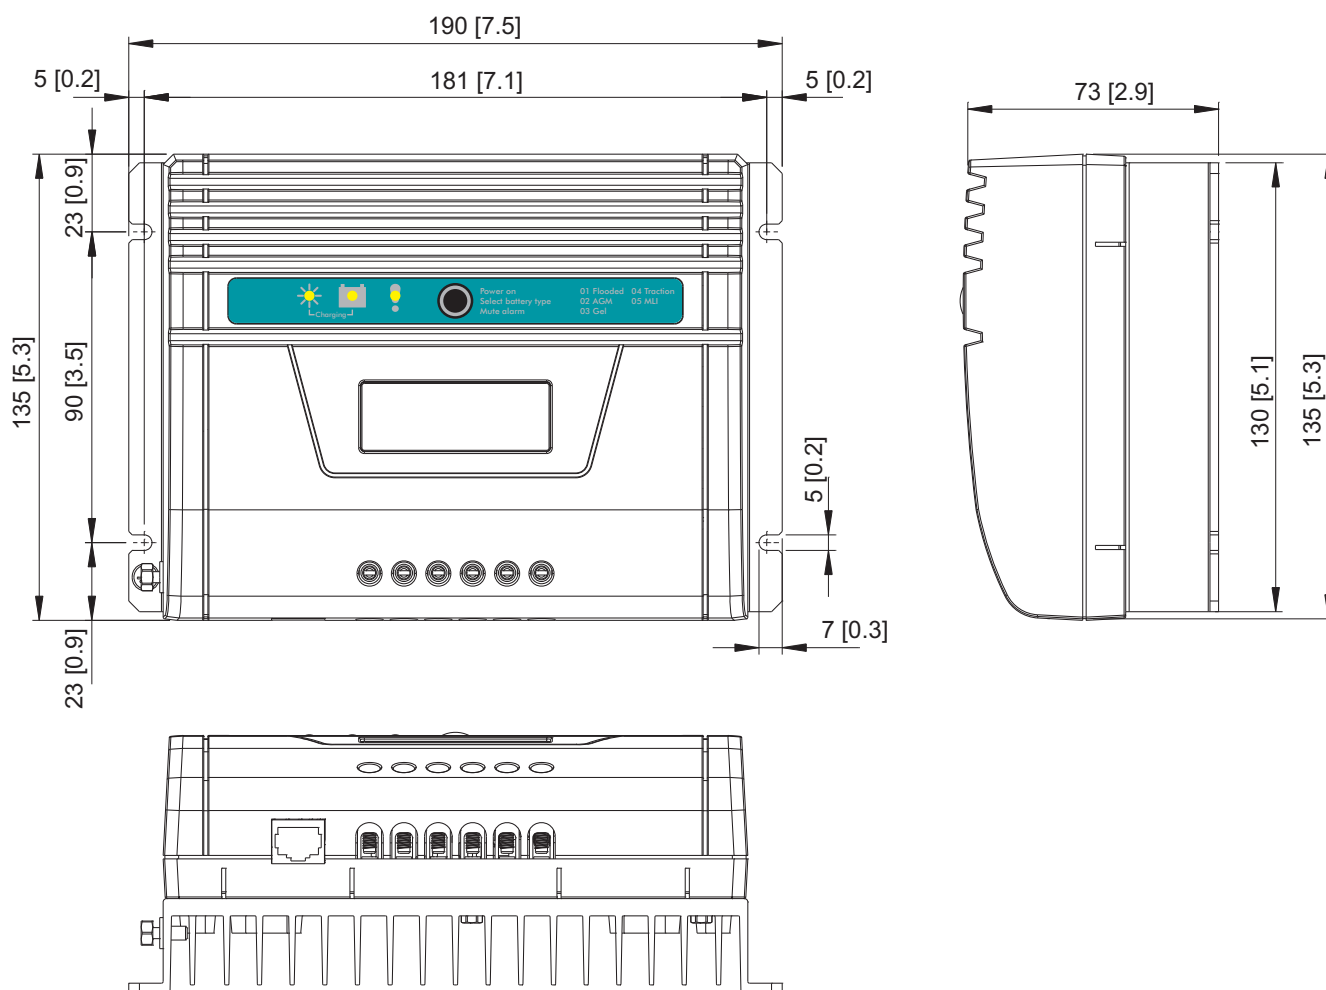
dimensions du Solar ChargeMaster en mm [pouces]
